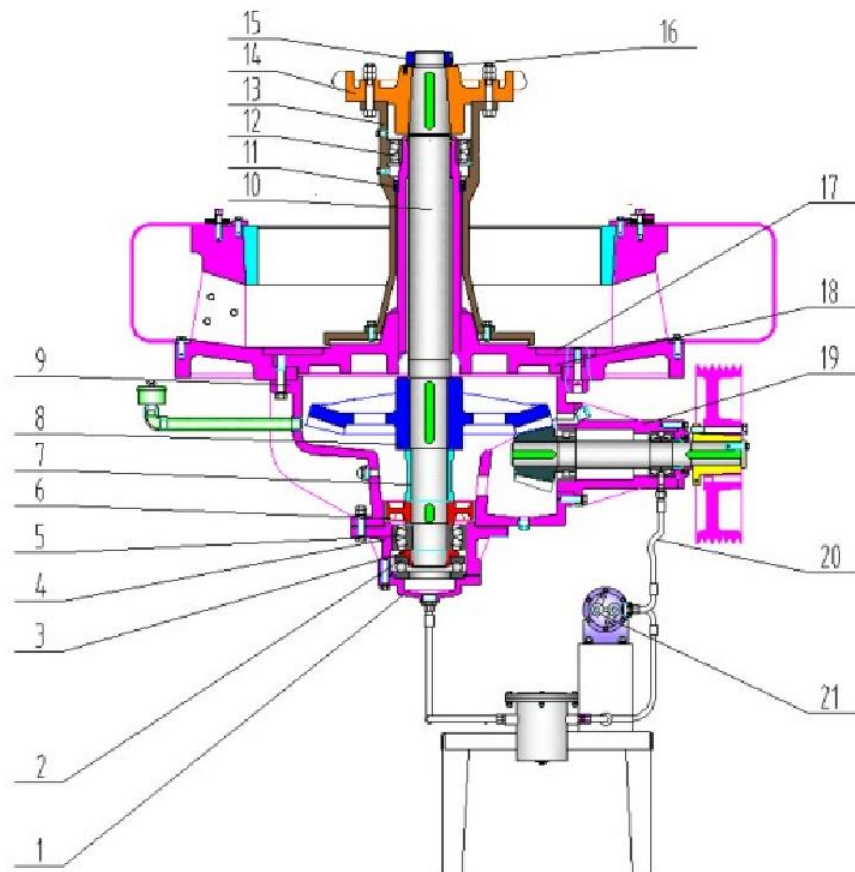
Установка редуктора и главного вала мельницы MTW 138
